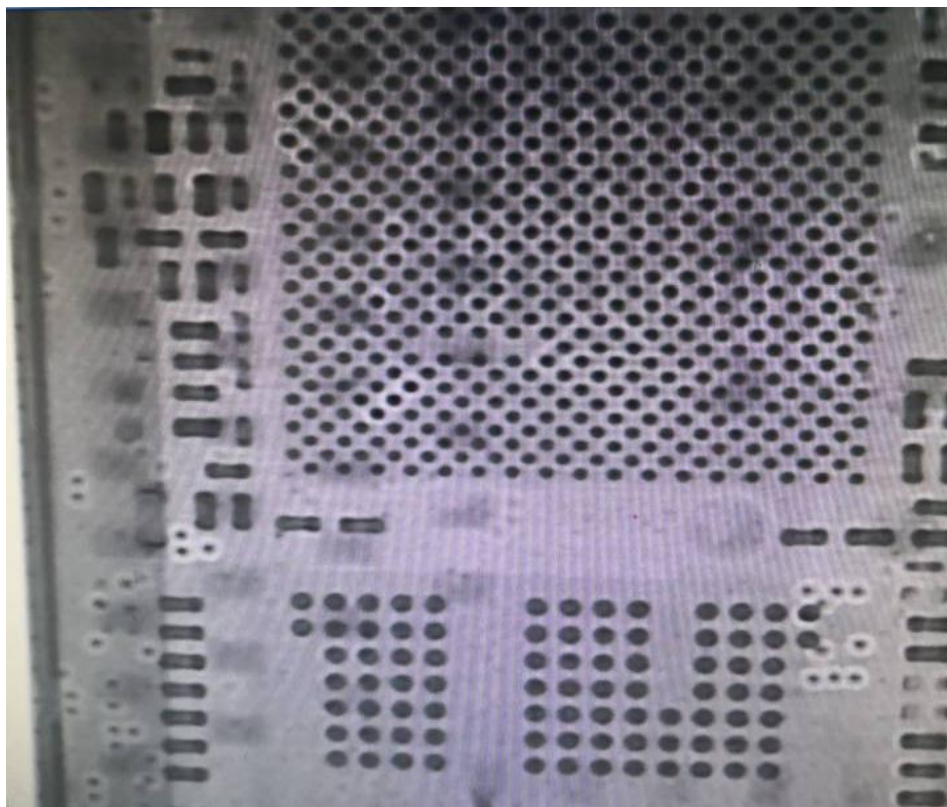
：模块底部引脚及 BGA 元件焊接状况检查
